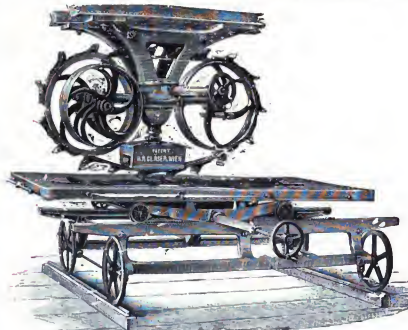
Ausstoß- oder Auswaschmaschine von H. R. Gläser, Wien.
